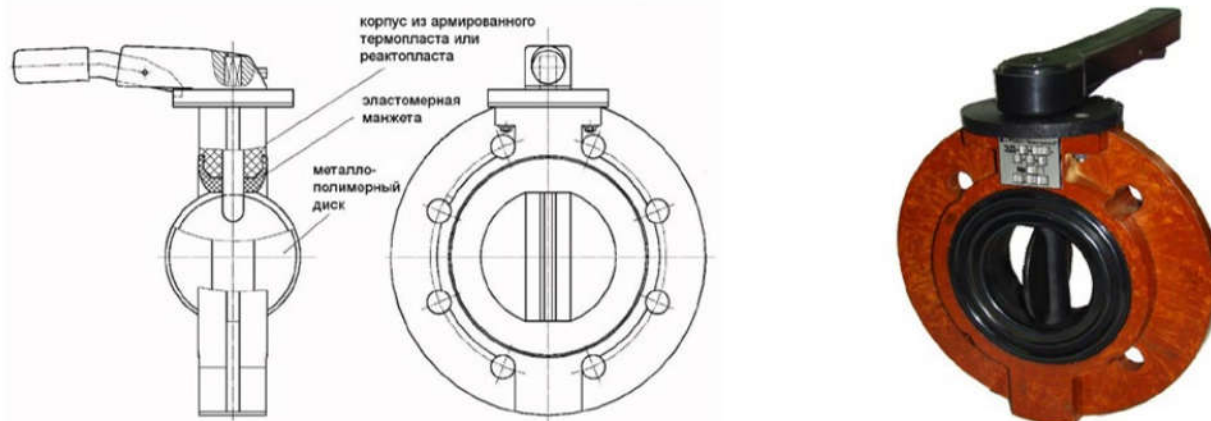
Схема и общий вид дискового затвора ЗД из композита «Констафтор Г» с эластичной манжетой.
